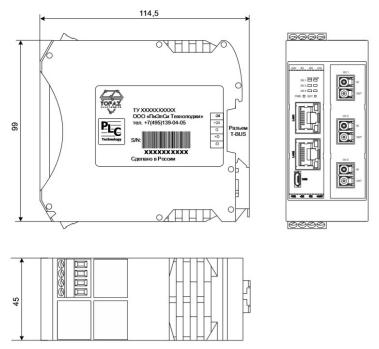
Внешний вид и габаритные размеры исполнения SGS-2Tx-3R-2LV
